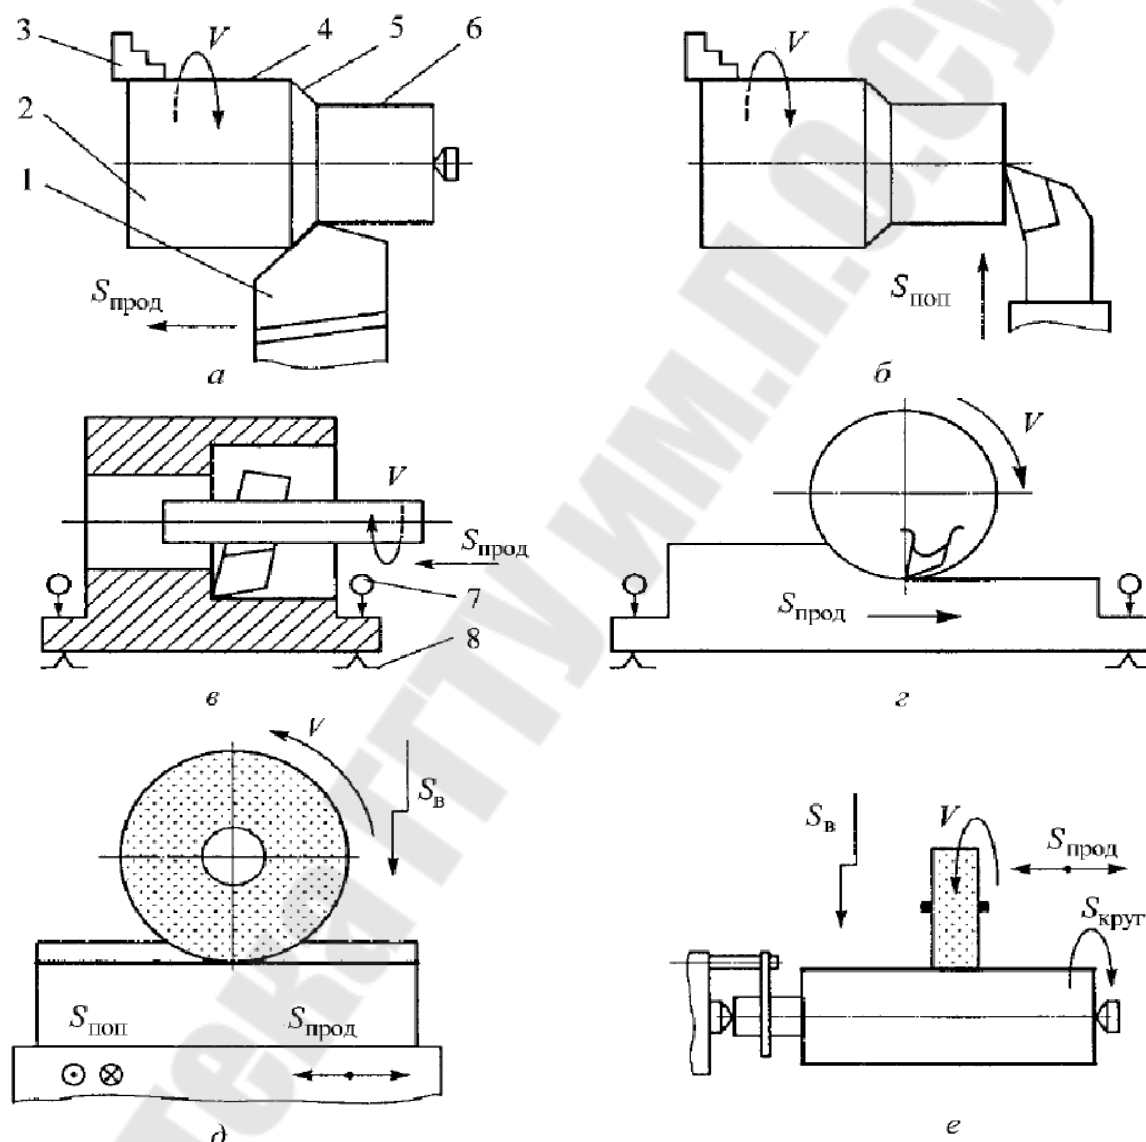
Схемы обработки заготовок: а – продольным точением; б – поперечным точением; в – растачиванием; г – фрезерованием; д – плоским шлифованием; е – круглым шлифованием: 1 – режущий инструмент; 2 – заготовка; 3 – станочное (рабочее) приспособление; 4 – обрабатываемая поверхность; 5 – поверхность резания; 6 – обработанная поверхность; 7 – прижим; 8 – базирующий элемент; V – движение резания; $S_{\text{прод}}$, $S_{\text{поп}}$, S_v , $S_{\text{крут}}$ – соответственно продольное, поперечное, вертикальное и круговое движения подачи
